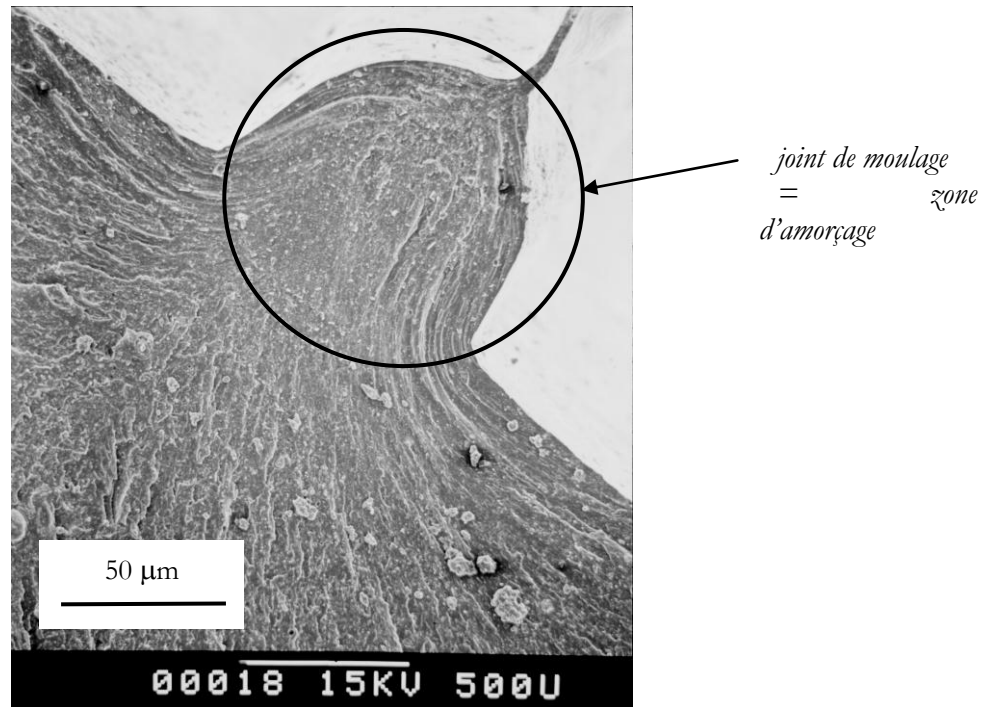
Essai AP7 – Amorçage sur le joint de moulage
